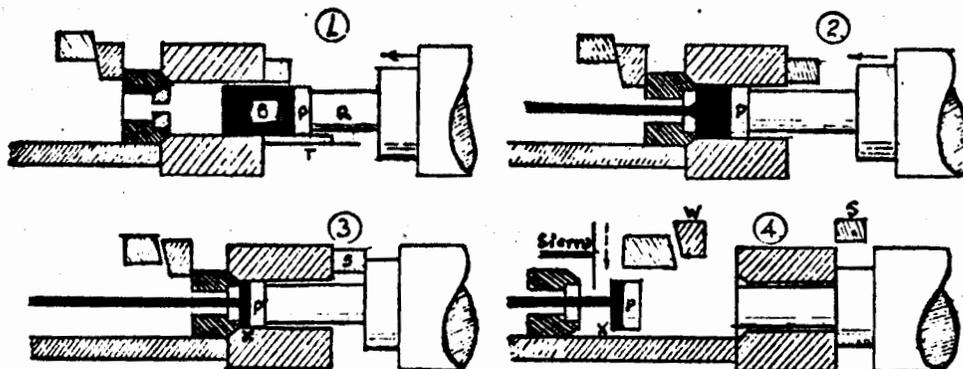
Ciclo de extrusión usando una prensa horizontal.
